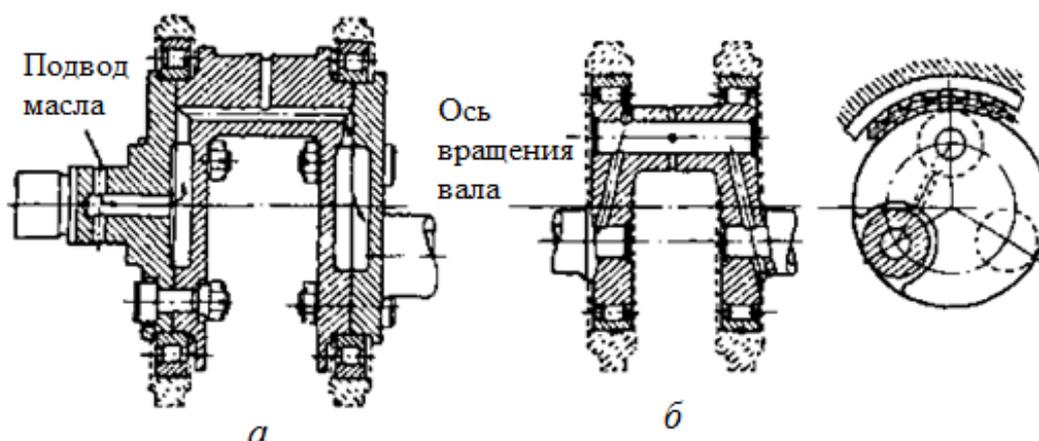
Установка составного (а) и монолитного (б) коленчатого вала на подшипники качения
